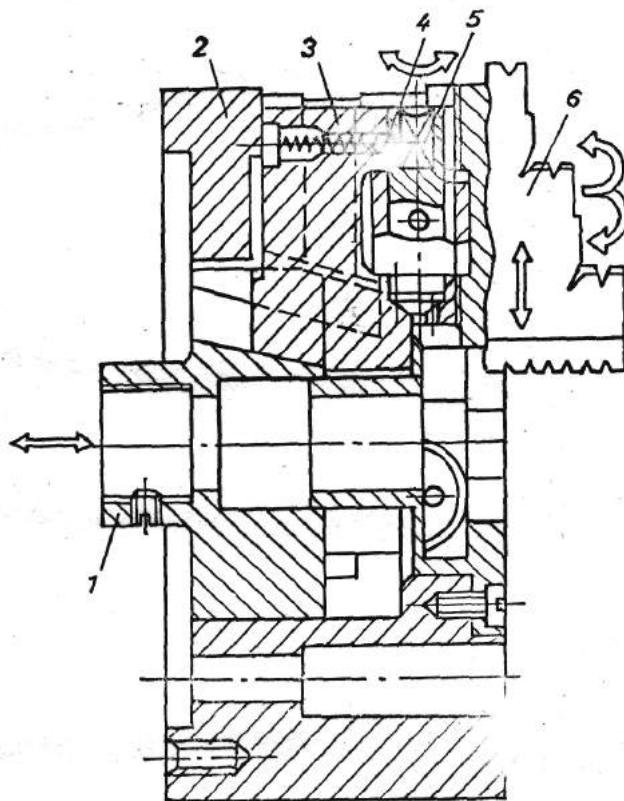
Клиновий швидкопереналагоджувальний патрон:
